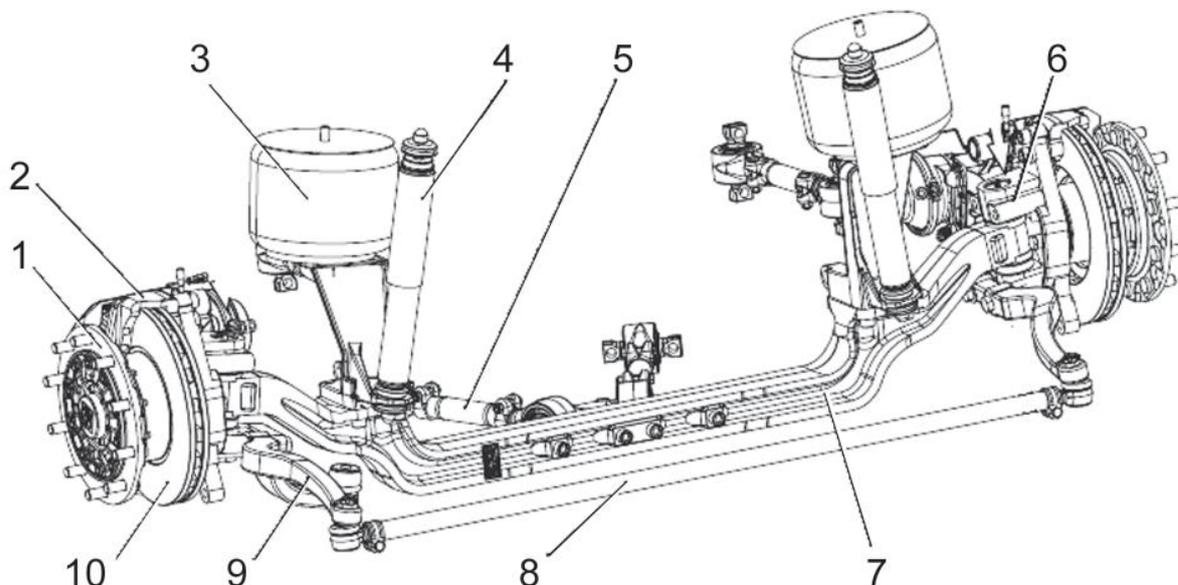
Передняя ось с реактивными штангами и пневмобаллонами подвески
